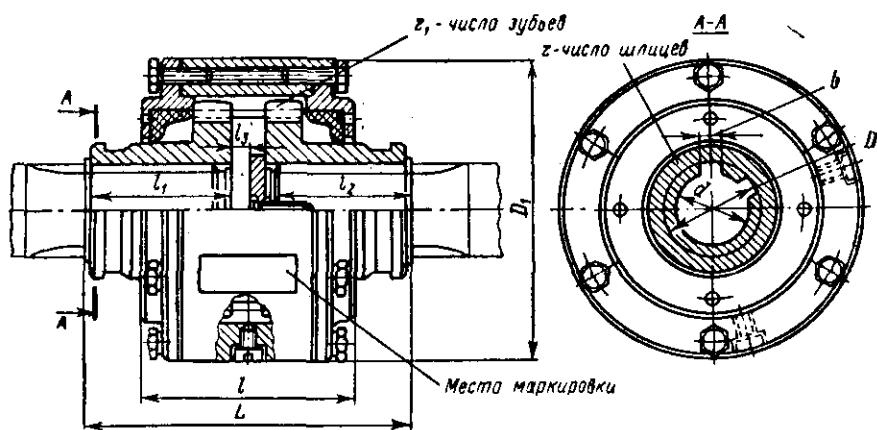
Зубчатые муфты регулировочно-соединительные: z — число шлицев; z_1 — число зубьев
